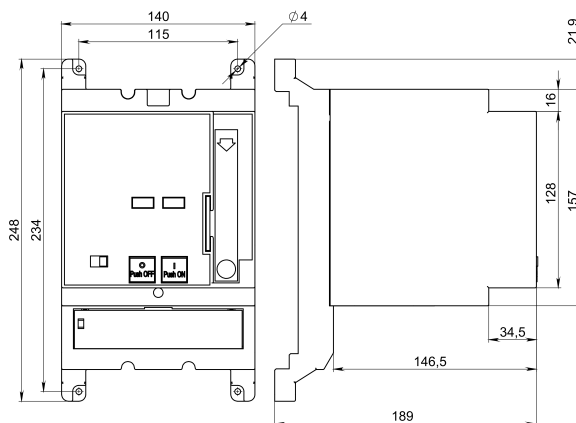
Габаритные и установочные размеры приводов ESMO T125-T160, T250
